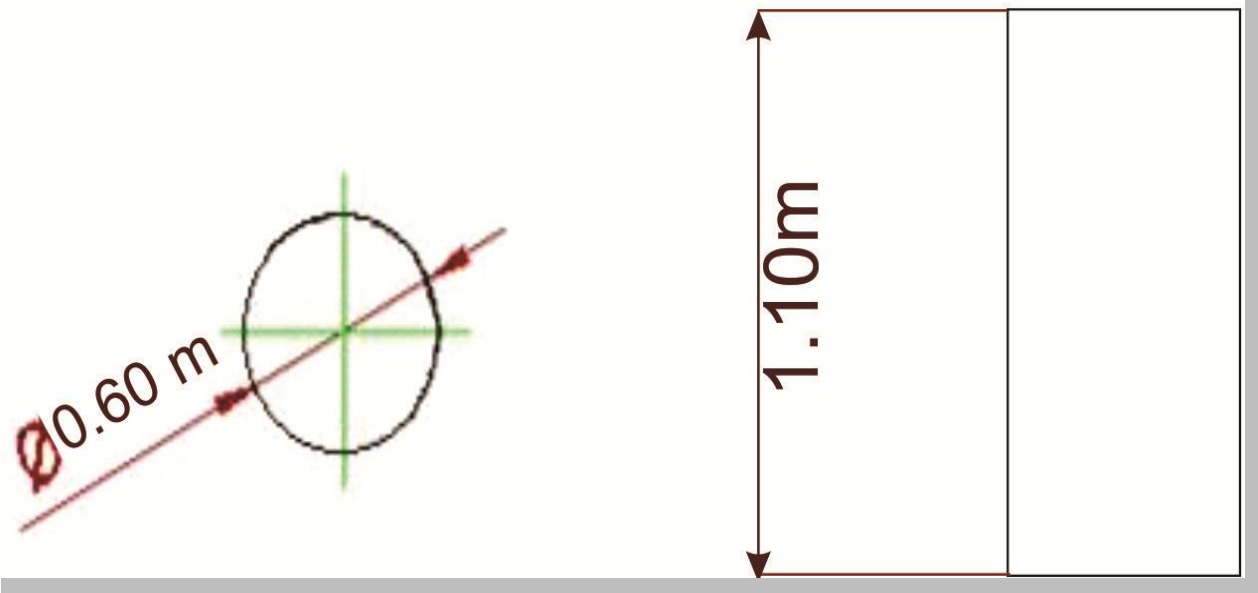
ESIME – 2011 - Dimensiones del Termo-tanque en vista lateral (izquierda) y superior (abajo).
